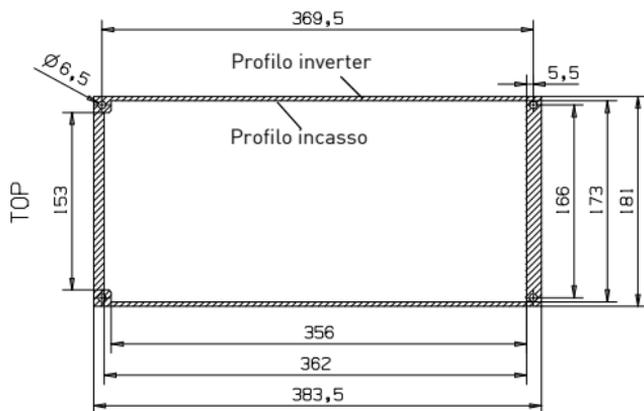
Misure dell'incasso per il montaggio a flangia per M14 (Unità: mm)
